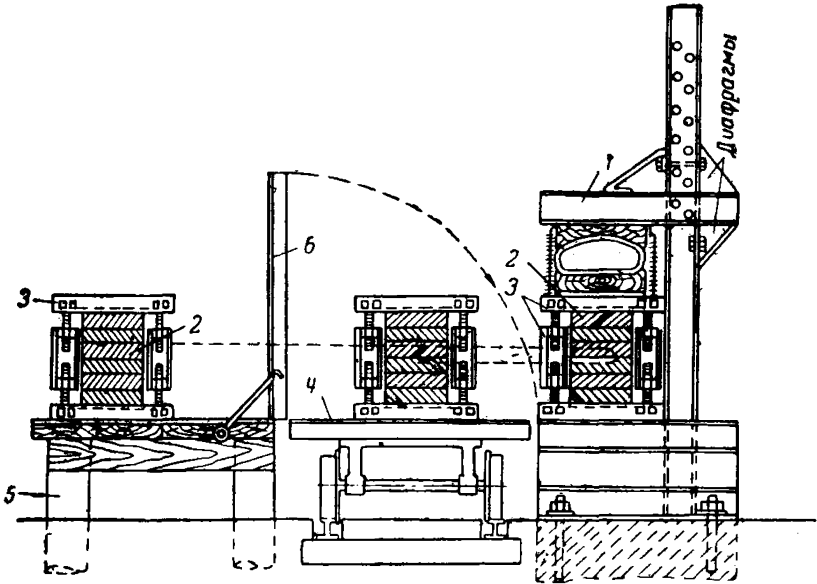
Схема пневматического пресса с применением дополнительных вайм
